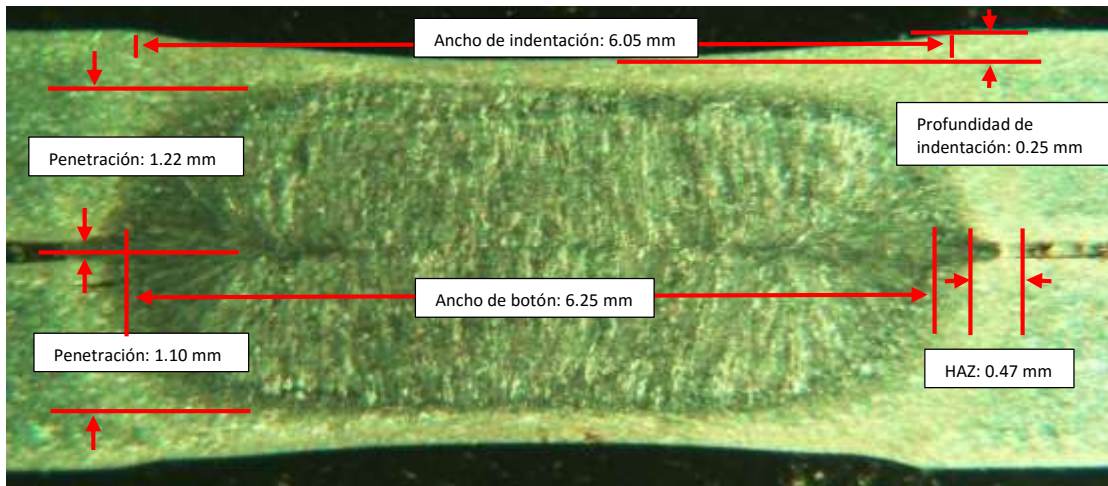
Mediciones realizadas en el botón de soldadura número 5.
